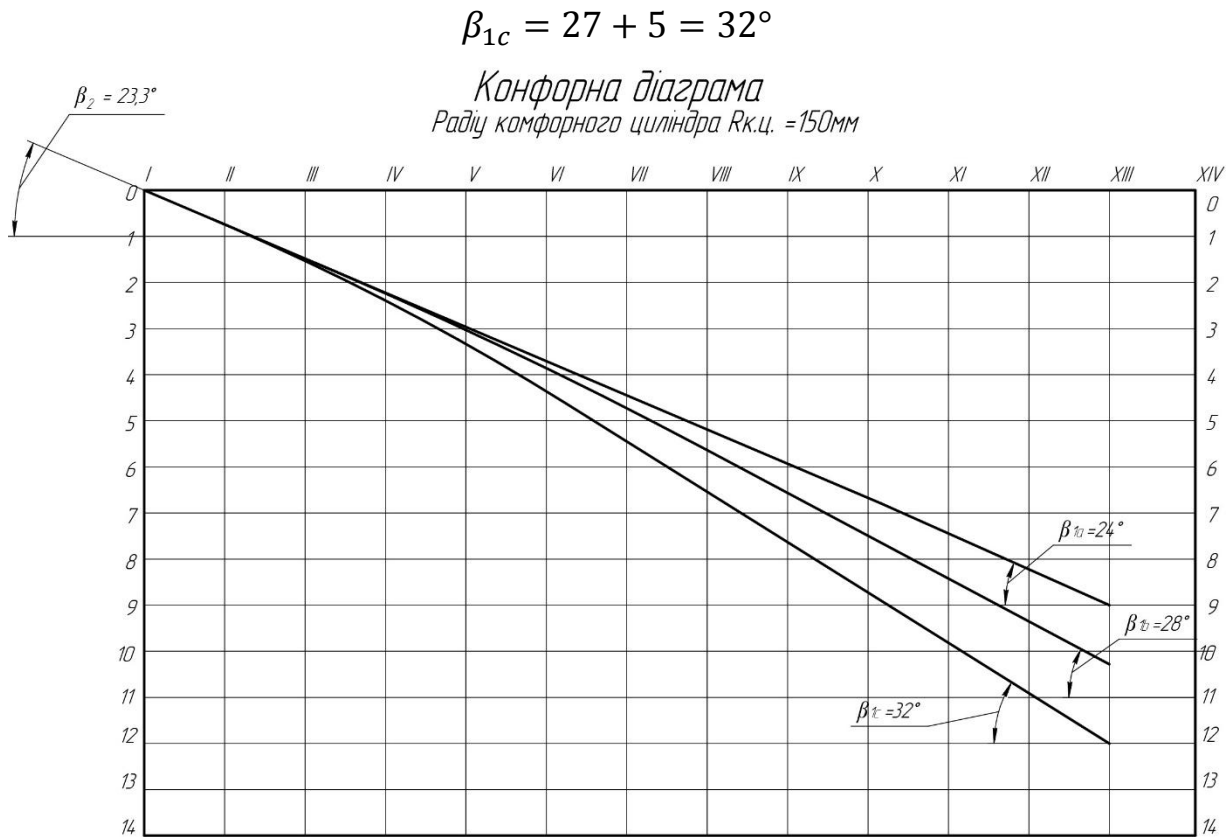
Профілювання поверхні лопаті на розгортці циліндра
